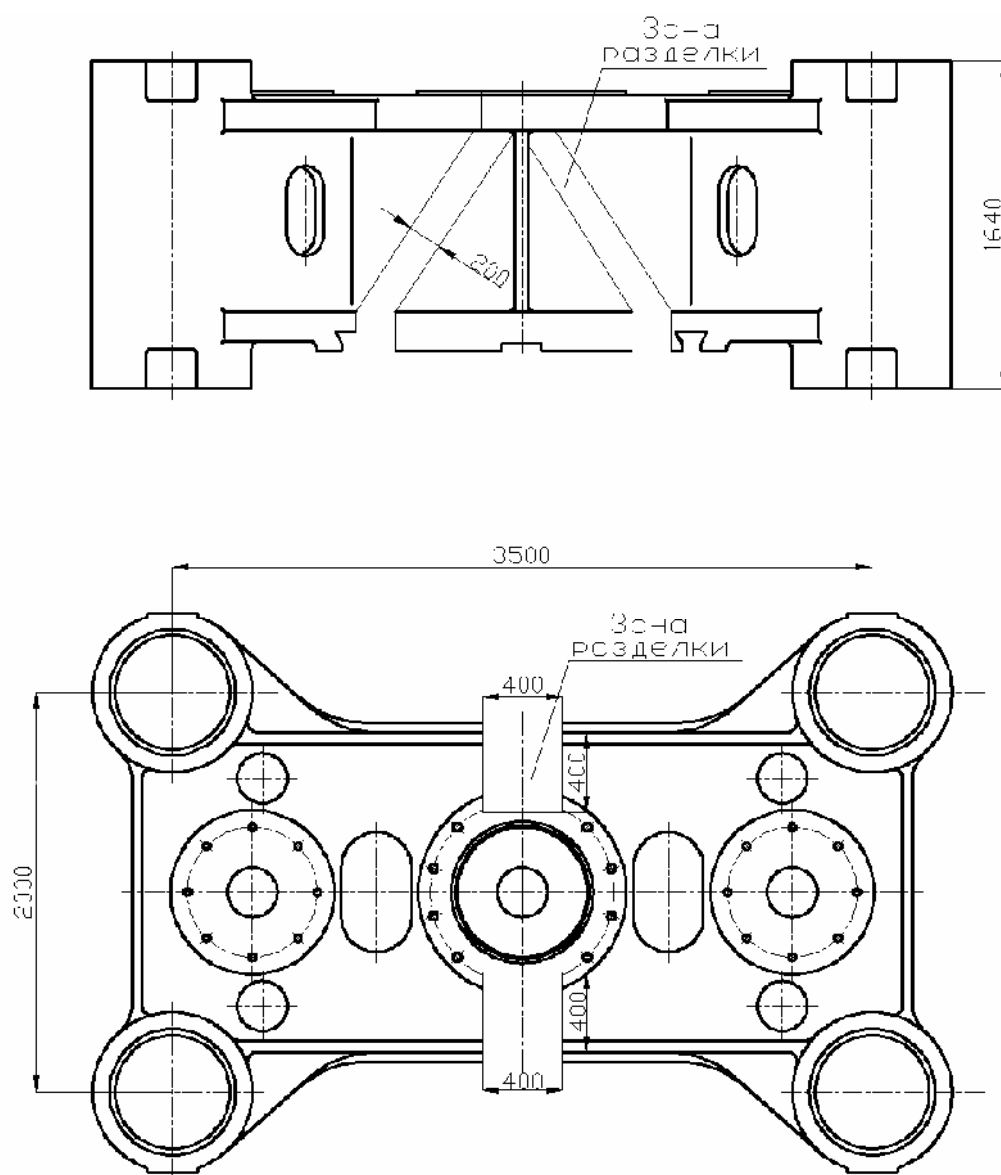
Разделка под сварку боковых стенок, верхнего и нижнего поясов подвижной поперечины ковочного прессы силой 32 МН
